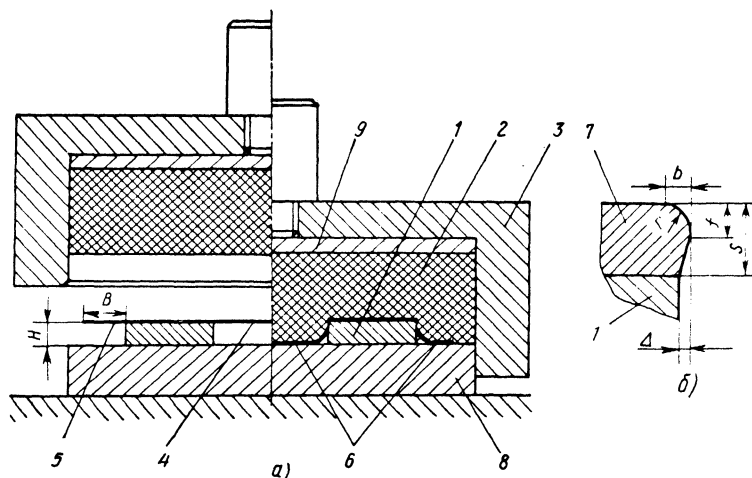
Вырубка-пробивка полиуретановым инструментом (а) и форма контура поверхности раздела после вырубki полиуретановым инструментом (б): 1 - шаблон; 2 - полиуретановая матрица; 3 - контейнер; 4 - листовая заготовка; 5 - припуск; 6 - отход; 7 - деталь; 8 - плита подштамповая; 9 - плита подкладная; b - утяжина продольная; f - утяжина поперечная;
